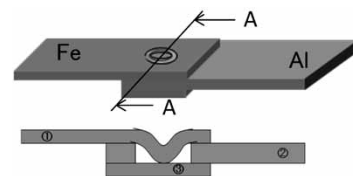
ダボスポット溶接されたTSS試験片の概念図
